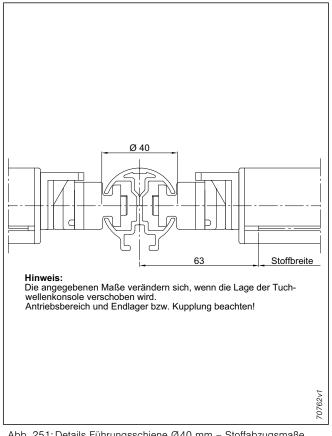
Details Führungsschiene Ø40 mm – Stoffabzugsmaße für Typ 101
